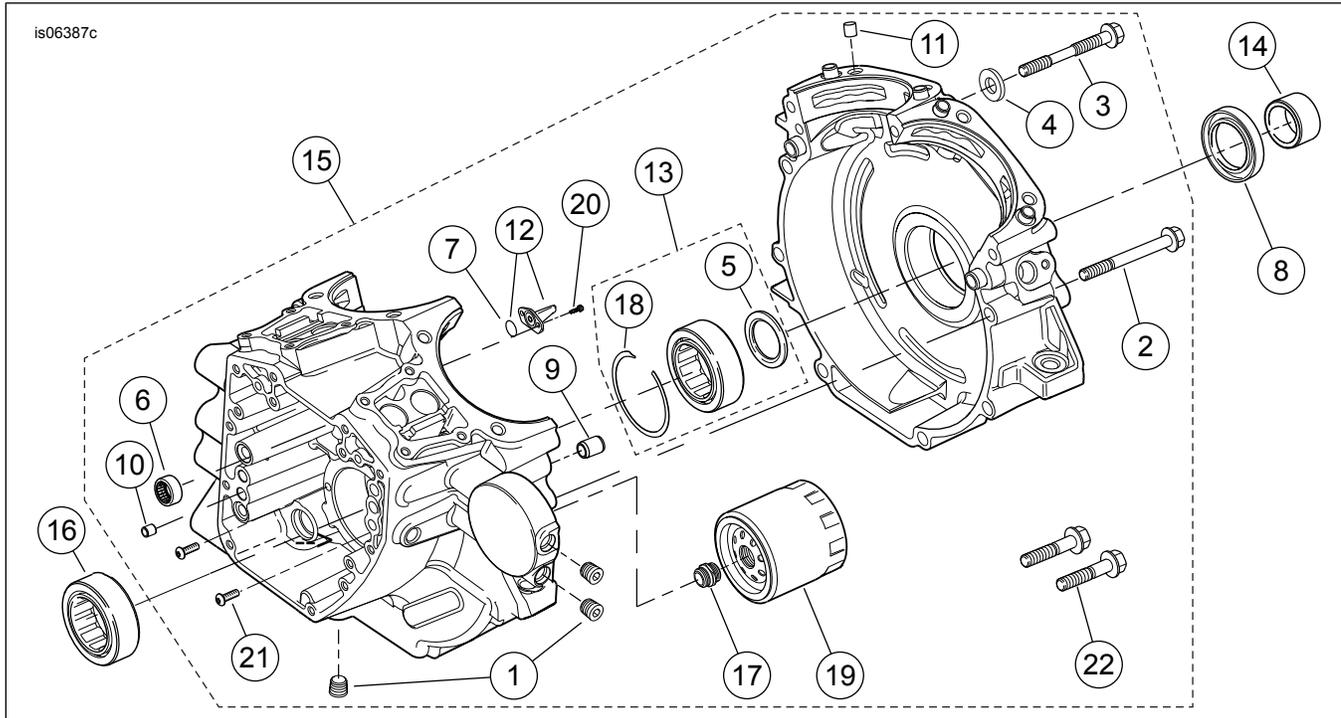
Kurbelwellengehäuse, Motorölfilter und -kühler – SE120ST Screamin' Eagle Crate-Motor
